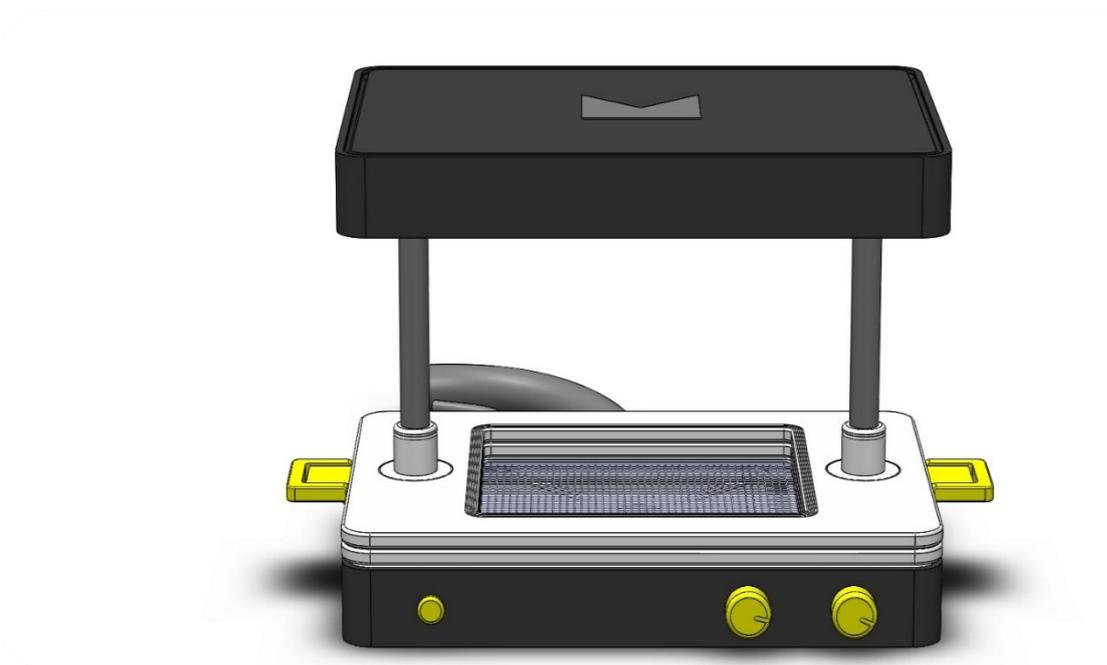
Vue d'ensemble en 3D de la machine du thermoformage sous-SolidWorks.
